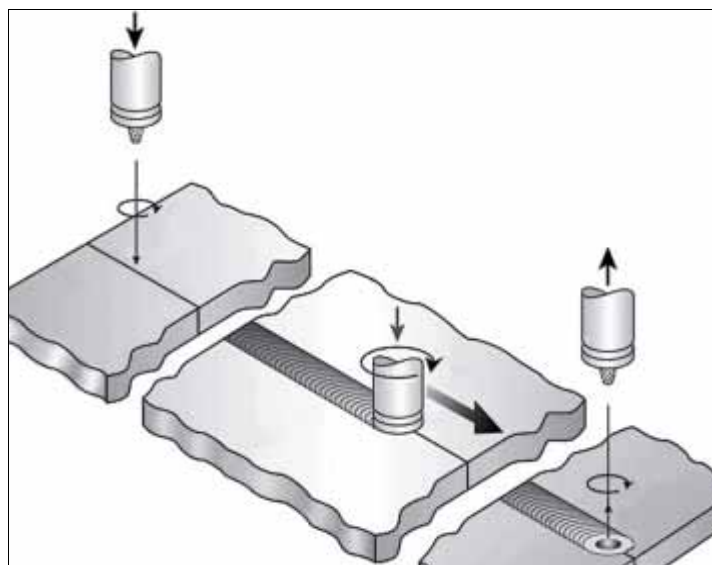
Présentation schématique du procédé friction stir welding (source: ISO 25239-1)
